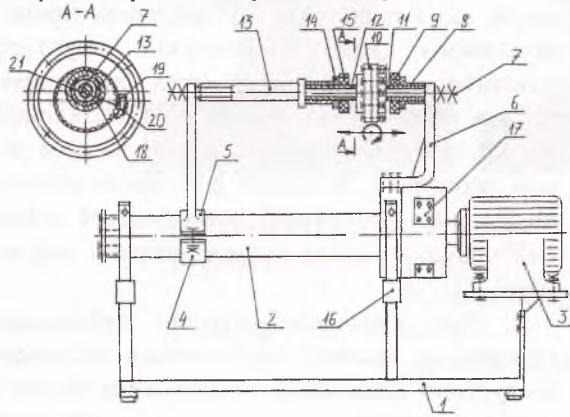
Принципова схема вібраційної машини для обробки методом ВВЗО.
